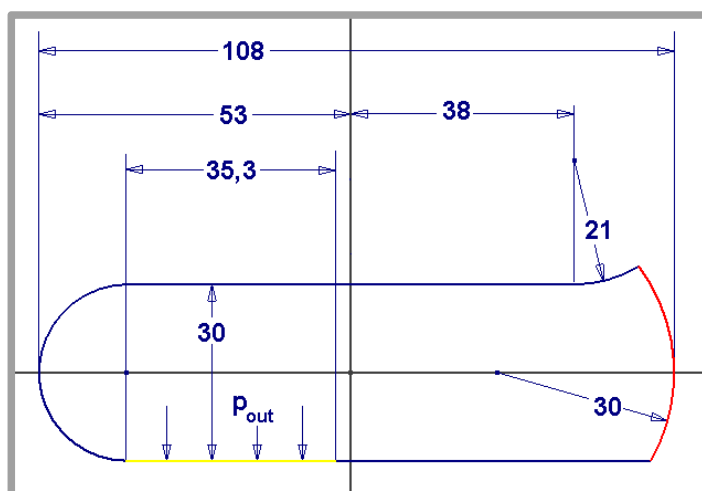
Diskový kompresorový jednosmerný ventil [17]
